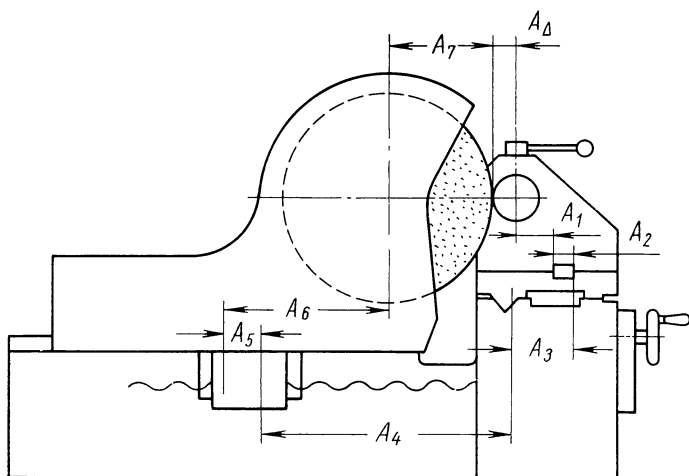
Схема одной из размерных цепей круглошлифовального станка
